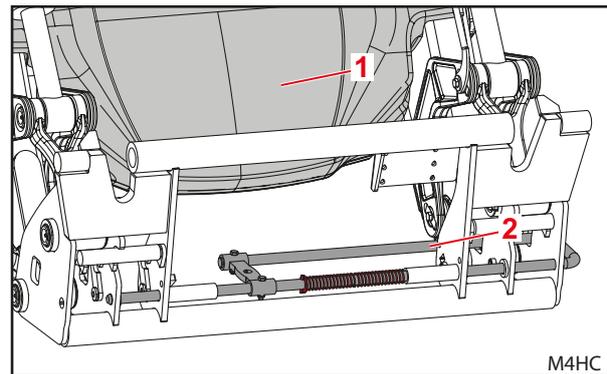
Smontare il dispositivo di bloccaggio meccanico degli attrezzi
